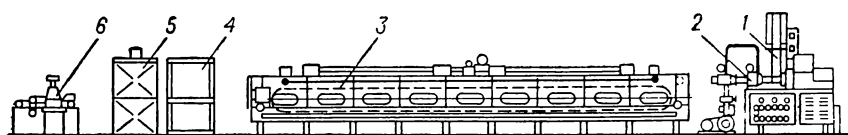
Схема установки для вулканизации неформовых изделий в расплаве солей:
